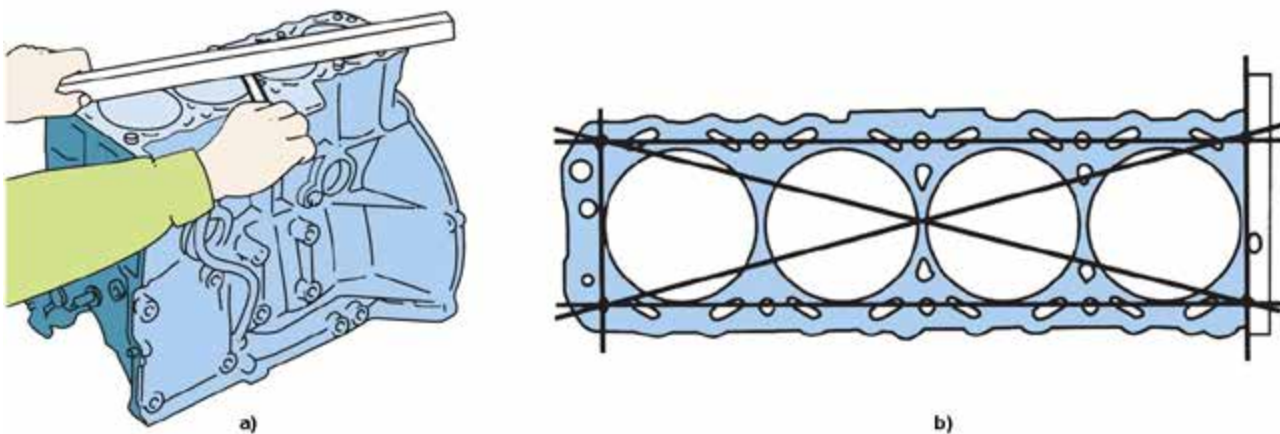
(а) Проверка плоскостности верхней поверхности блока цилиндров проверяется с помощью поверочной линейки и набора плоских щупов. (б) Чтобы получить уверенность, что поверхность блока цилиндров идеально ровная, следует провести измерения в шести направлениях, как это показано на прилагаемом рисунке; источник: *Pearson Education, Inc.
